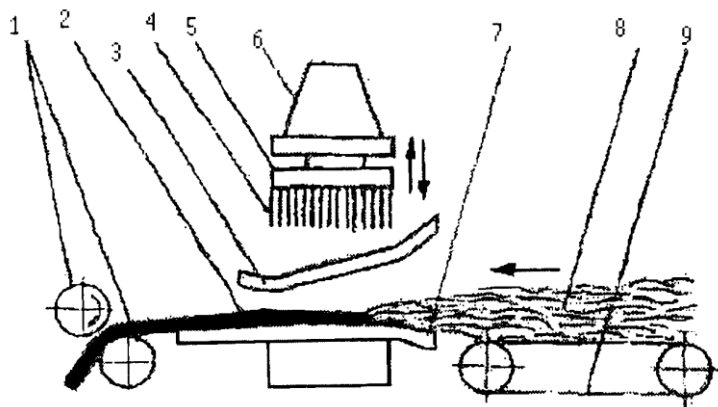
Принципова схема робочої зони голкопробивної машини
